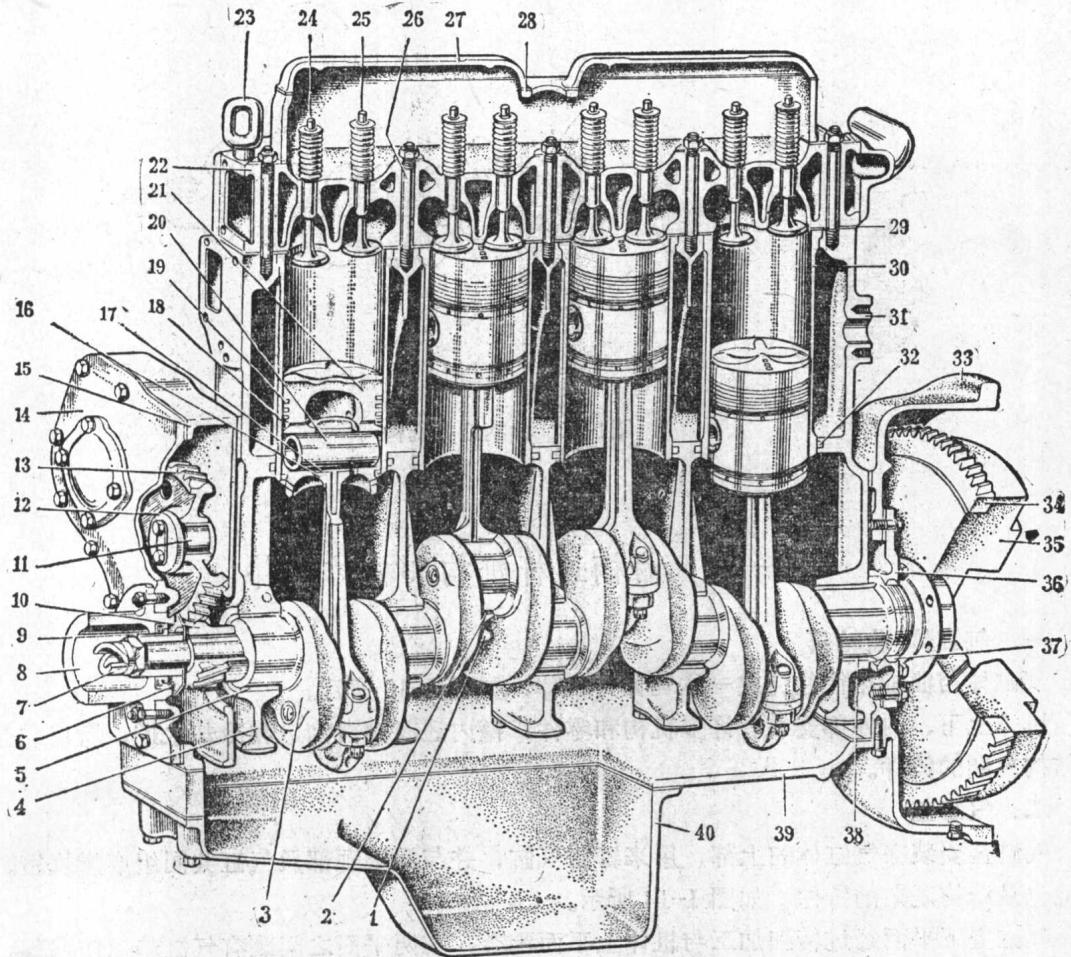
4125A型柴油机的曲柄连杆机构和机体零件图
